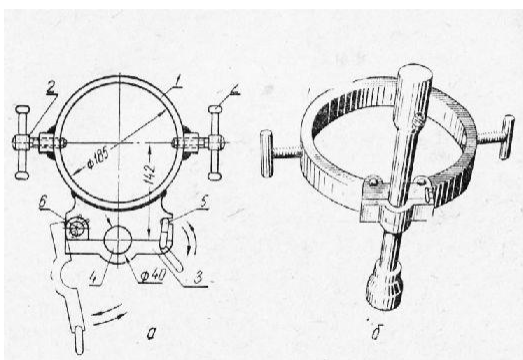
Приспособление для облегчения отвертывания гаек колес грузовых автомобилей: а — конструкция; б — применение; 1 — кольцо; 2 — фиксатор; 3 — планка; 4 — отверстие под ключ; 5 — серьга; 6 — ось
